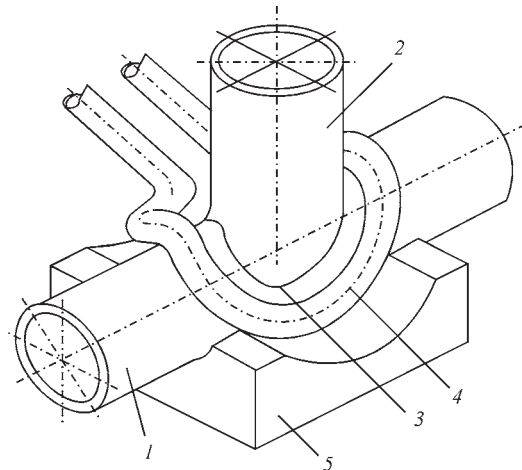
Схема процесу індукційного зварювання тиском із застосуванням активуючих речовин Т-подібного з'єднання: 1 – основна труба; 2 – відвідна труба; 3 – місце розташування активуючих речовин; 4 – розташування робочого органу – індуктора; 5 – частина зварювального обладнання (упор)
